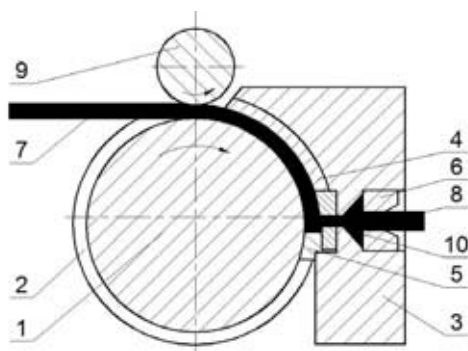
Схема конформ с расширяющейся форкамерой: 1 – рабочее колесо; 2 – ручей колеса; 3 – башмак; 4 – кольцевая вставка; 5 – опорная вставка; 6 – матрица; 7 – заготовка; 8 – изделие; 9 – прижимной валок; 10 – форкамера
